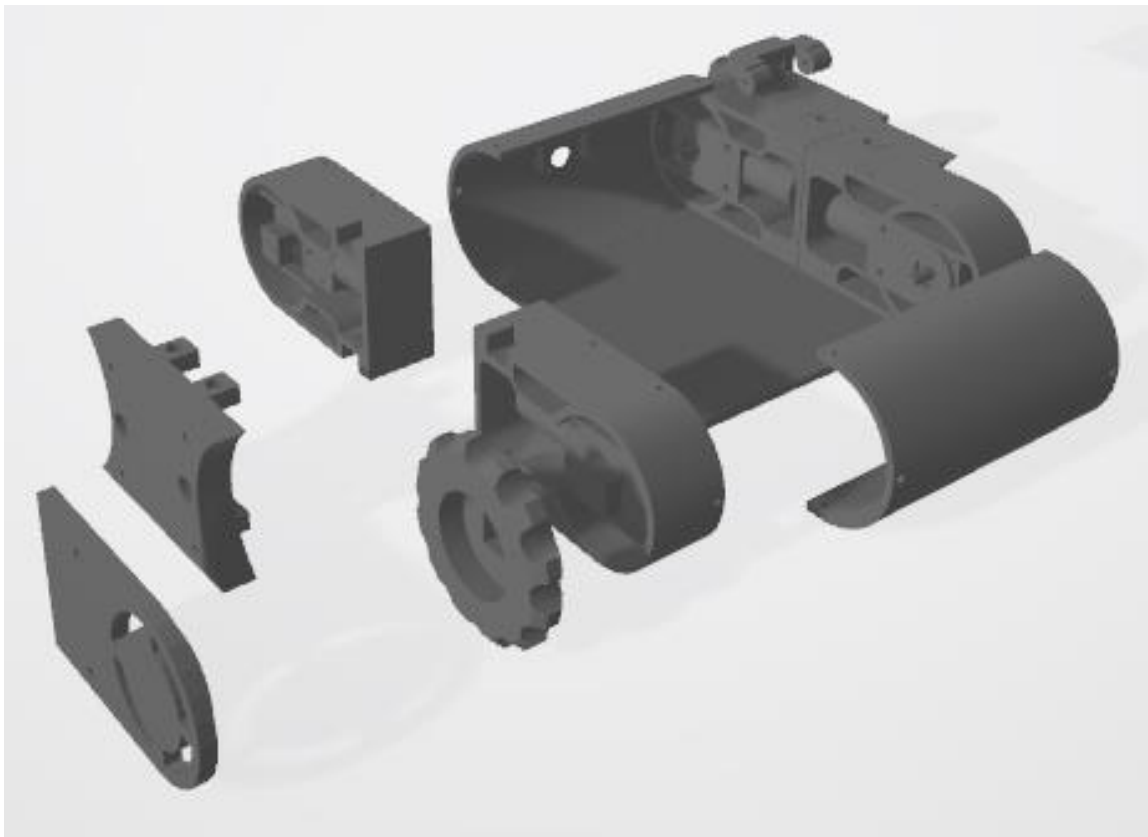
"Explosion " 3D модель зборки мобільного робота
